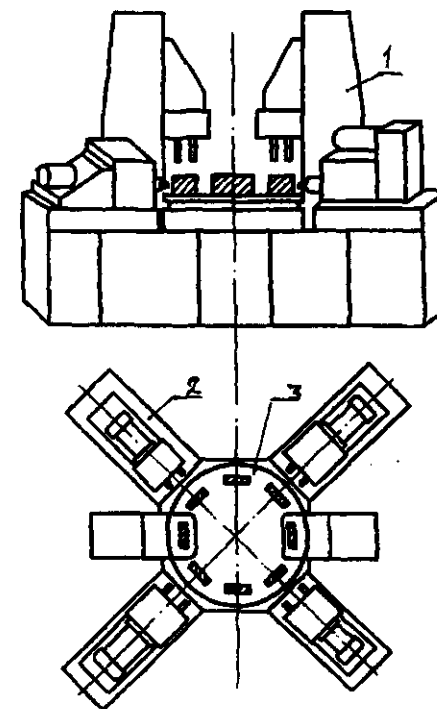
Компонировка агрегатного станка с делительным поворотным столом: 1 — вертикальная головка (2 шт.); 2 — горизонтальная головка (4 шт.); 3 — восьми позиционный делительный поворотный стол
